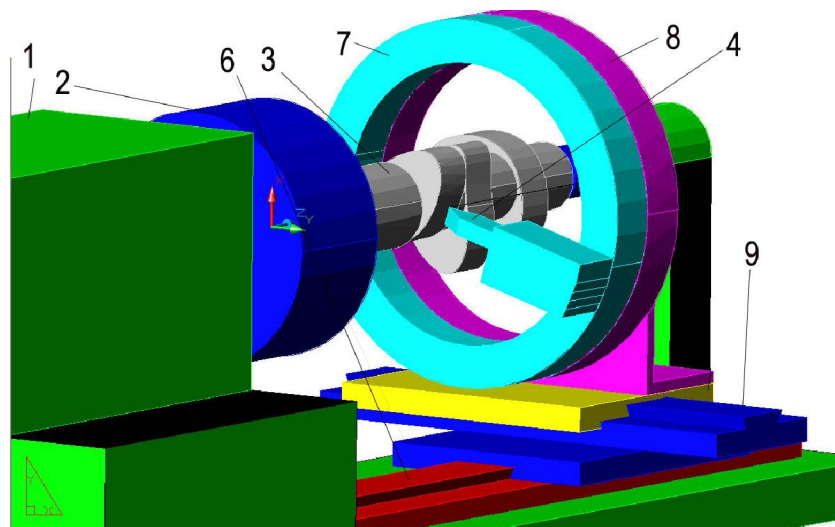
Configurarea strungului în vederea prelucrării unei suprafețe profilate transversal
